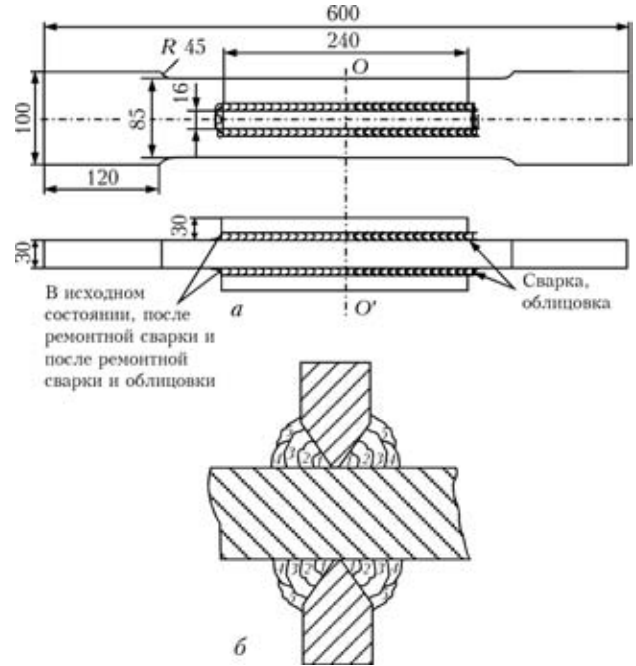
Схема образца для оценки эффективности облицовки швов проволокой X10Ni10 на сопротивление усталости новых и отремонтированных сварных соединений при одночастотном нагружении (а) и схема сварки (б): 1 — первый проход (корень шва); 2 — сердцевина; 3 — заварка разделки кромок с использованием электродов УОНИ-13/55; 4, 5 — облицовочные швы, выполненные проволокой X10Ni10 в углекислом газе
